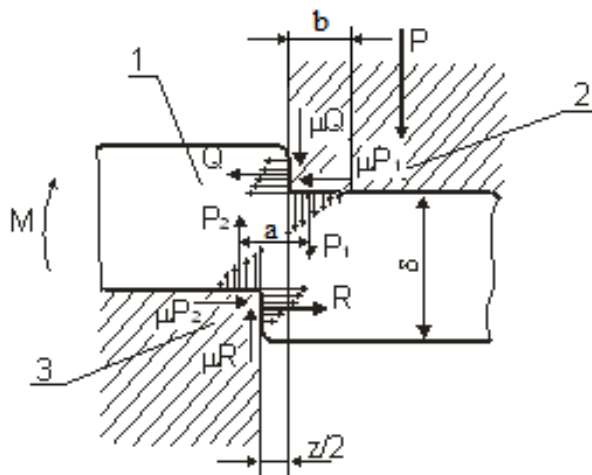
Схема сил, действующих на заготовку при вырубке: 1 – заготовка; 2 - режущая кромка пуансона; 3 – режущая кромка матрицы
